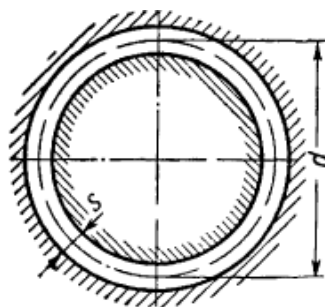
Коаксиальный цилиндрический зазор в разрезе
